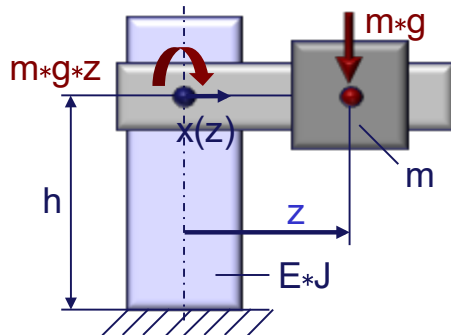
Wirkung des Eigengewichtes bei bewegten Baugruppen durch „wandernde Lasten“
